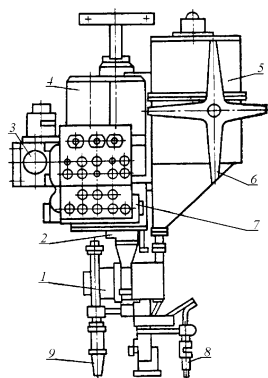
Сварочный автомат типа А-1401: 1 – механизм подачи электродной проволоки; 2 – суппорт поперечной настройки; 3 – самоходная тележка; 4 – штанга; 5 – флюсоаппарат; 6 – кассета с электродной проволокой; 7 – механизм подъема; 8 – светоуказатель; 9 – флюсоотсос
